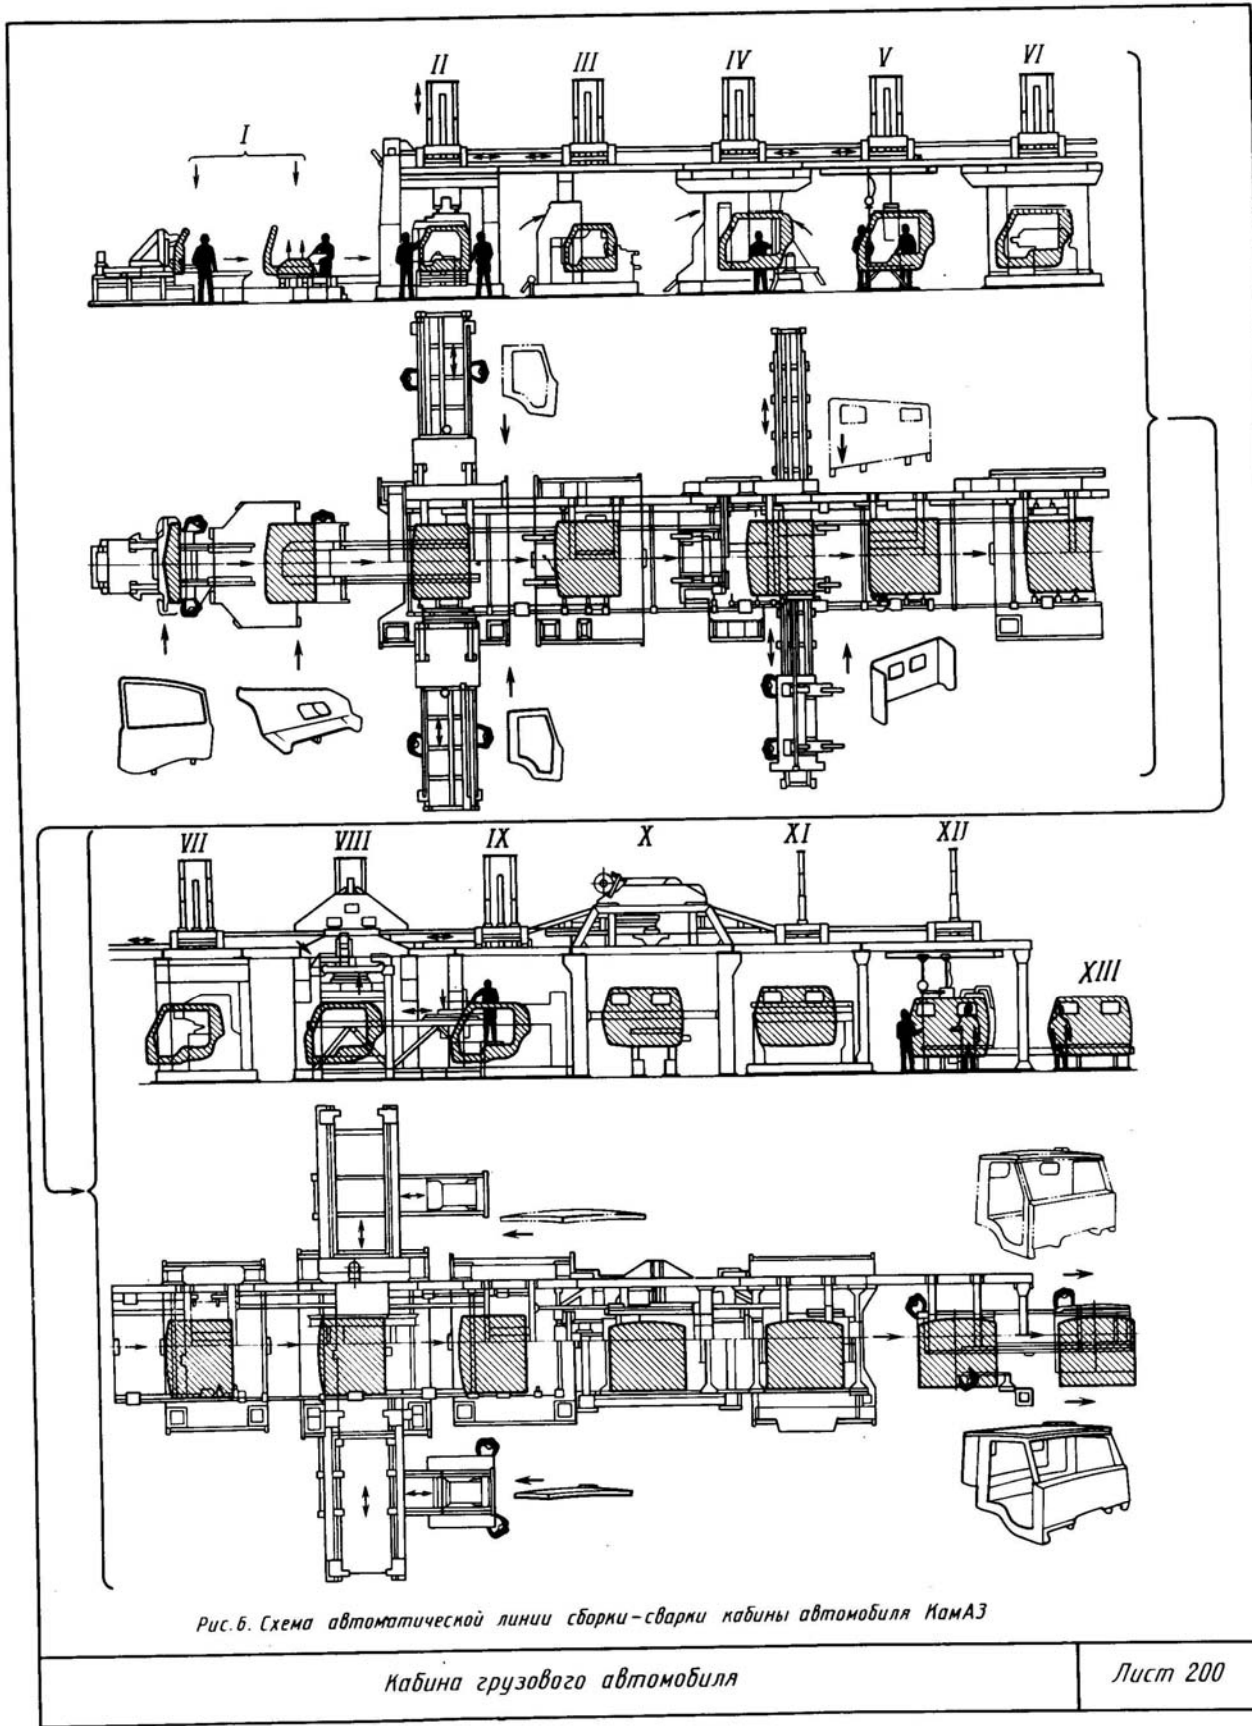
Схема автоматической линии сборки-сварки кабины автомобиля КамАЗ
